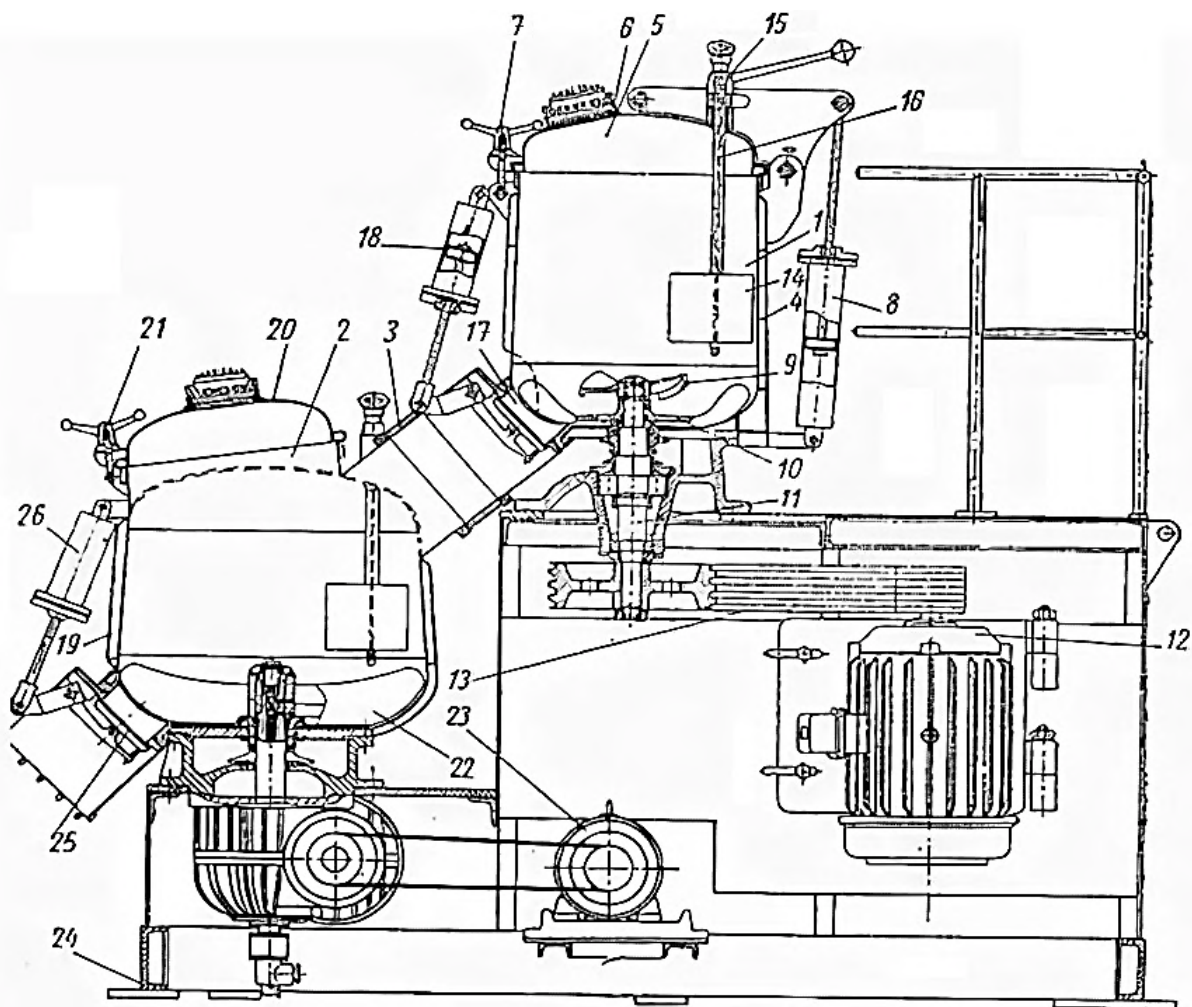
Двухстадийный турбоскоростной смеситель:
